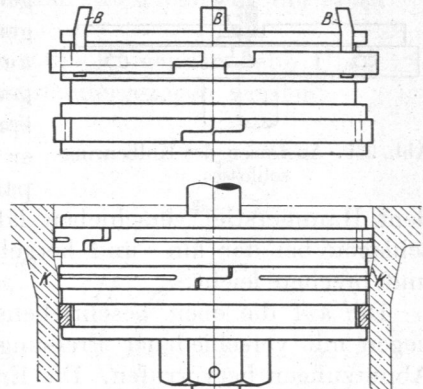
und 956. Aufziehen der Kolbenringe und Einführen derselben in die Zylinderfläche.
